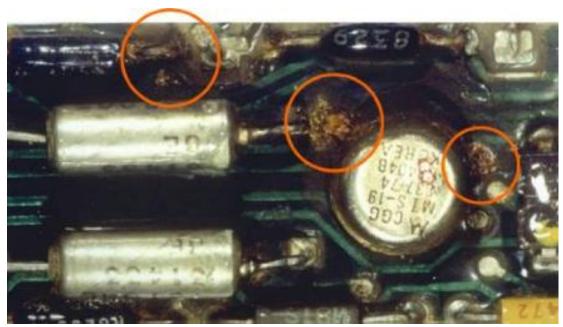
Efecto De La Corrosión En Puntos De Soldadura
